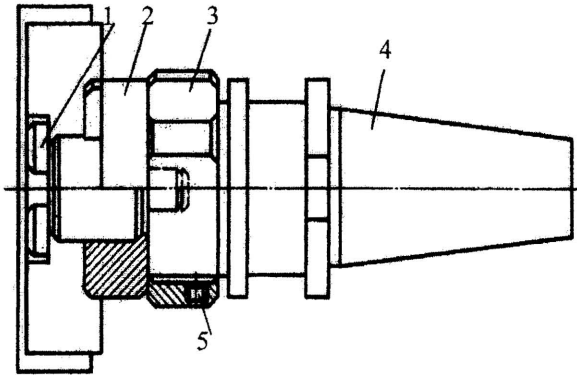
Оправка для крепления торцовых фрез и зенкеров диаметром до 125 мм
